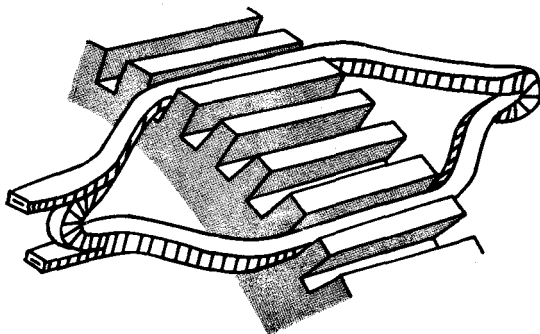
Disposición de las secciones del arrollamiento de un inducido de tambor.
